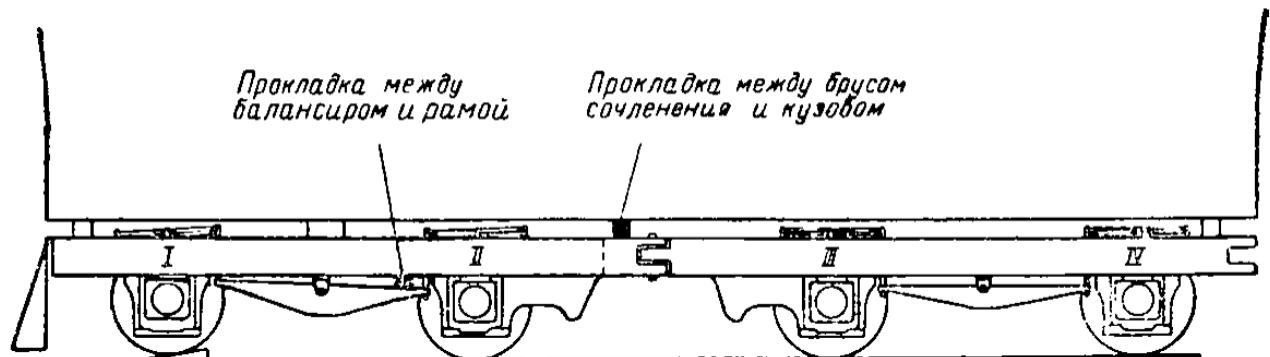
Расположение приспособлений при уменьшении нагрузки на первую колесную пару
